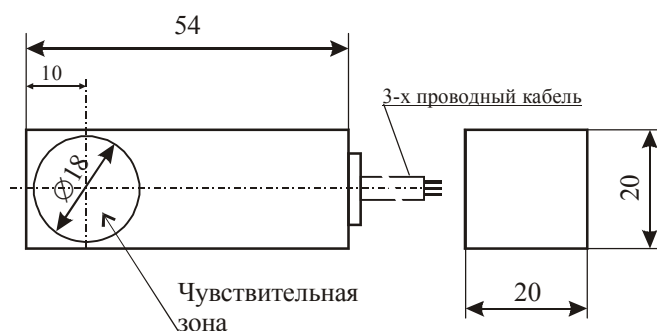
Внешний вид и габаритные размеры датчиков типа СМВ2-П20М-02-000
